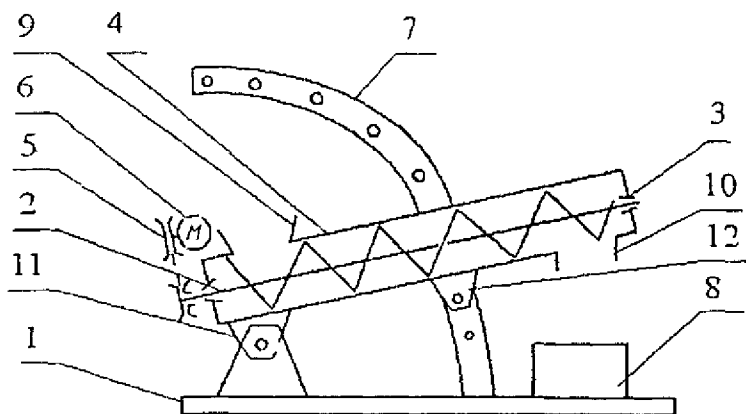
Учебный прибор для демонстрации работы винтового конвейера: 1 – рама; 2 – винтовые витки; 3 – подшипники; 4 – цилиндрический кожух; 5 – ременной вариатор; 6 – электродвигатель; 7 – дуга; 8 – емкость; 9 – загрузочное окно; 10 – разгрузочное окно; 11, 12 – кронштейны
